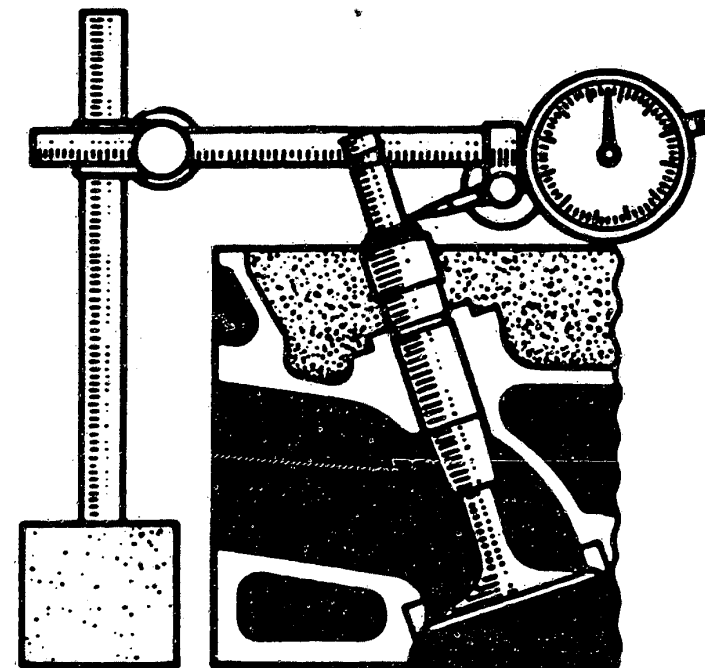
Das Ermitteln des Ventilschaft-Laufspiels bei eingebautem Ventil hat möglichst nahe an der Führung zu erfolgen.
